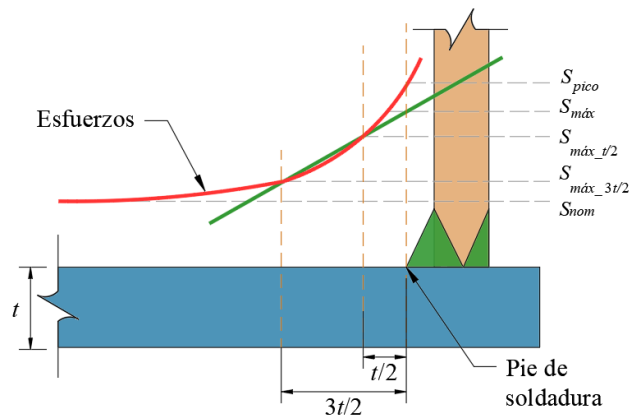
Gradiente de esfuerzos en la vecindad de la soldadura: real e idealizado con interpolación lineal
